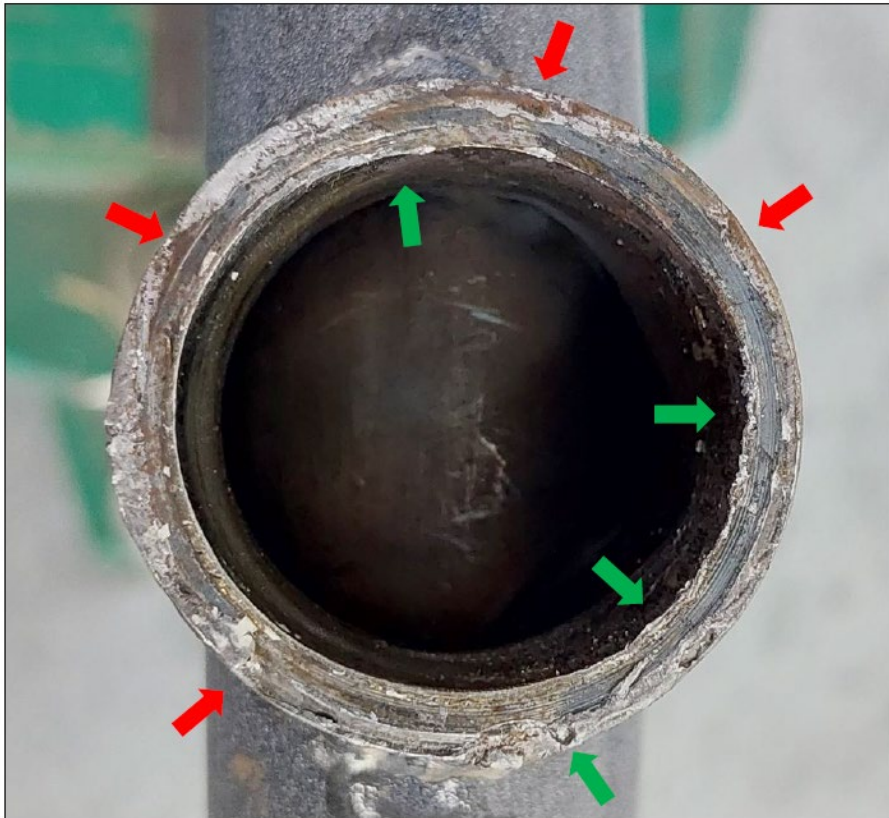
Inspección de la zona de falla de la horquilla del tren de nariz. Fuente:
